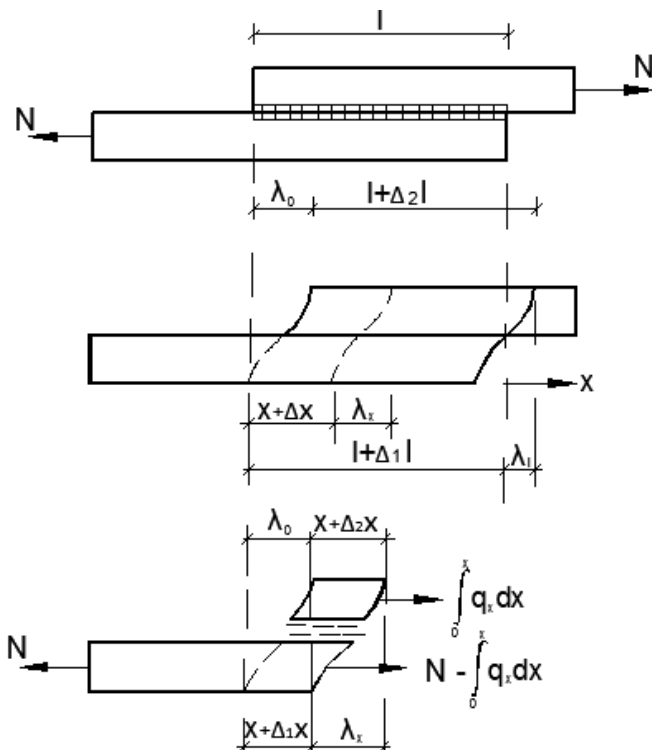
Схема загрузки и деформации сварного соединения
